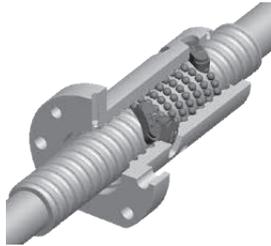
Kugelgewindemutter mit interner Einzelrückführung
